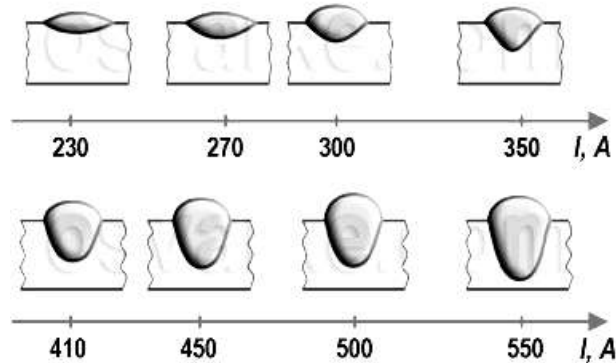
Вплив зварювального струму на форму й розміри зварного шва
